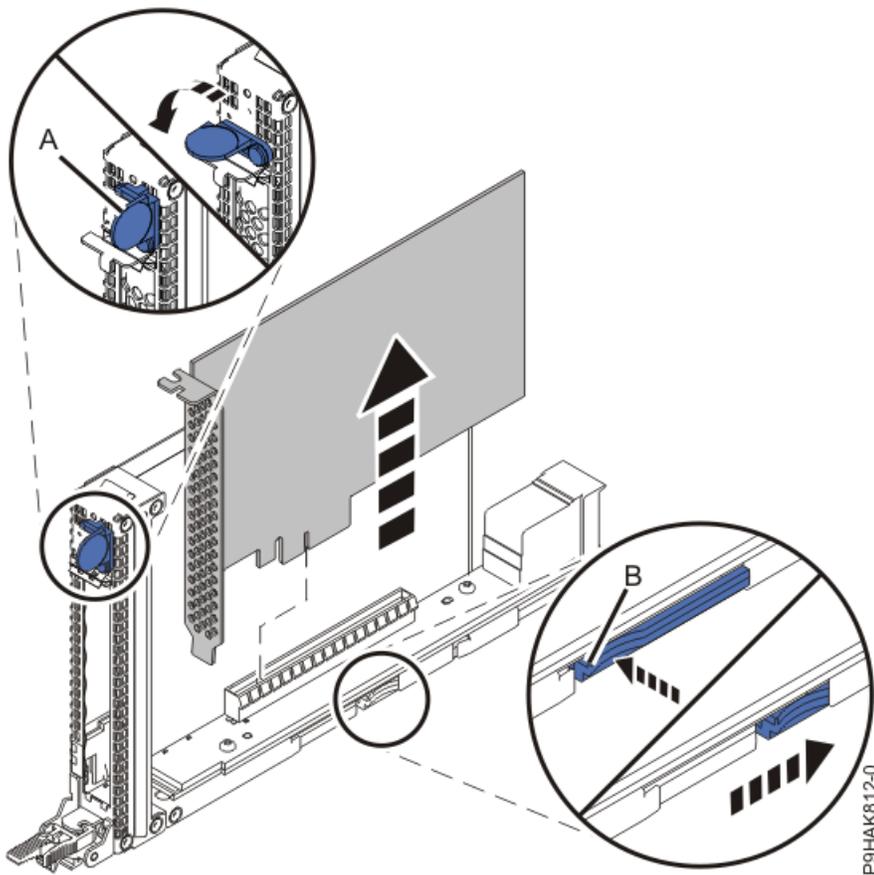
Remover um adaptador de uma cassete para o sistema 9040-MR9
